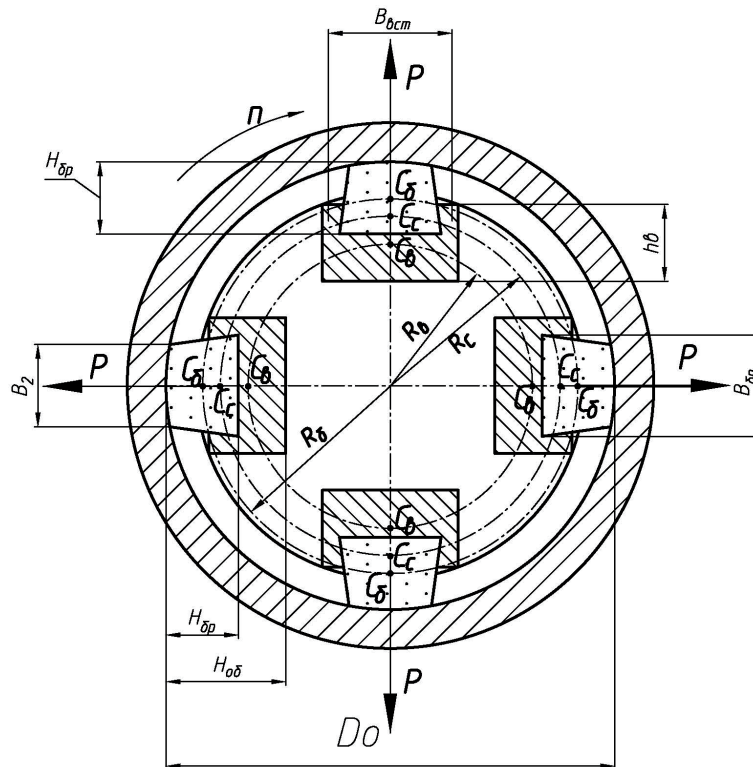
Схема компоновки головки хонинговальной центробежной для определения конструктивных параметров
